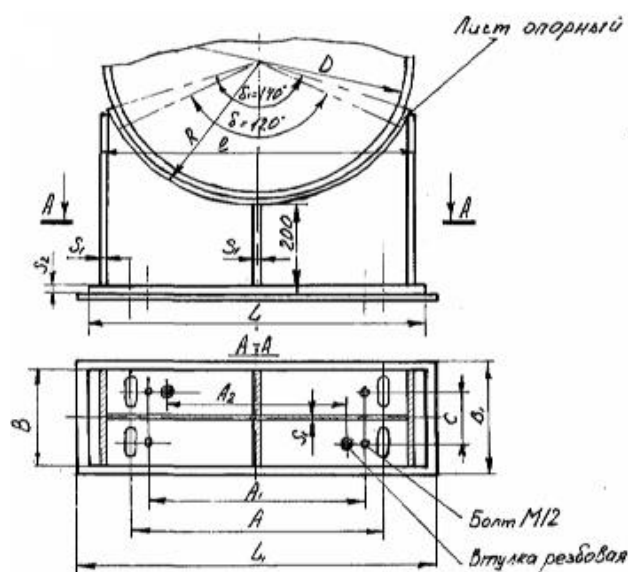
Конструкция стандартных седловых опор под стальные сварные горизонтальные цилиндрические аппараты.
